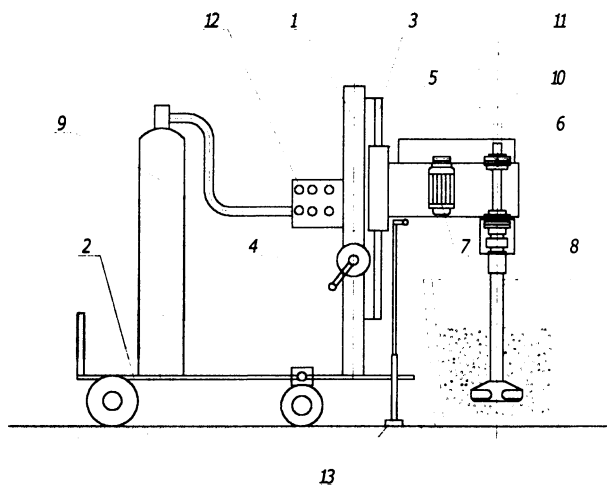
Установка для продувки расплава передвижная: 1 — опорная колонна; 2 — передвижная платформа; 3 — направляющие; 4 — ручная лебедка; 5 — каретка; 6 — траверса; 7 — привод; 8 — ротор; 9 — баллон; 10 — муфта; 11 — бачок-дозатор; 12 — пульт управления процессом; 13 — домкрат-тормоз
